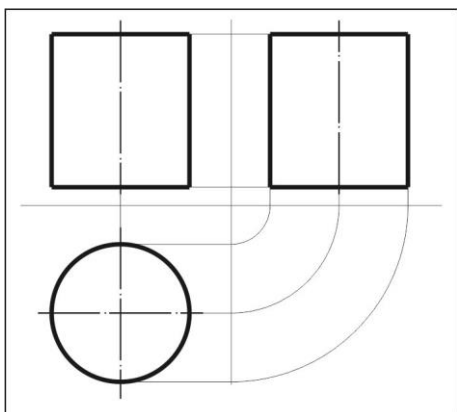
Комплексный чертеж прямого кругового цилиндра
